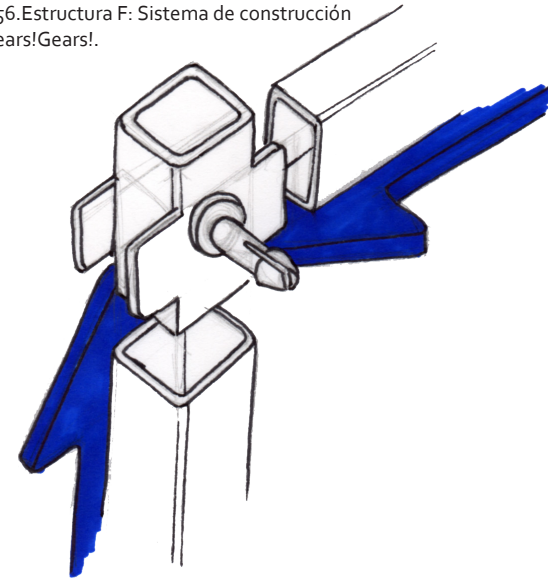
Estructura F: Sistema de construcción Gears!Gears!Gears!.
